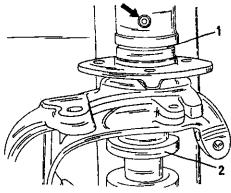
Запрессовка ступицы колеса. Перед опусканием пуансона (1) подставить подкладку (2) под внутреннее кольцо подшипника.
